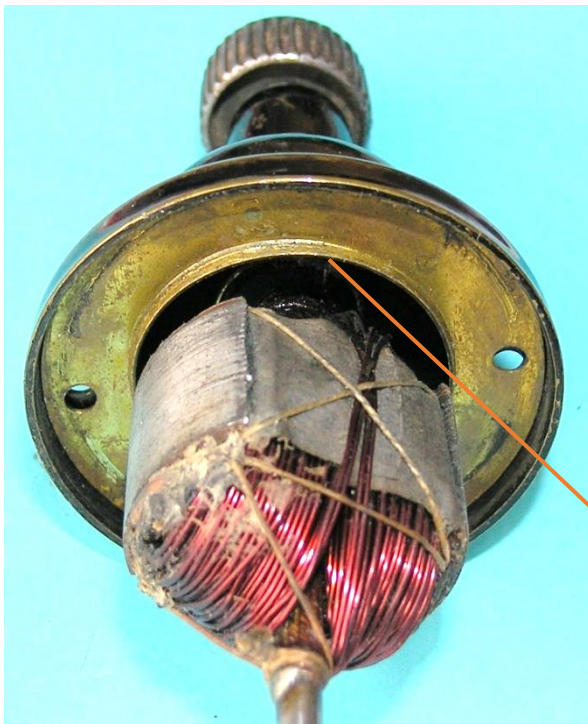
Schraubelemente für die Befestigung des Gehäusetopfes am Lagerhalsfuß
